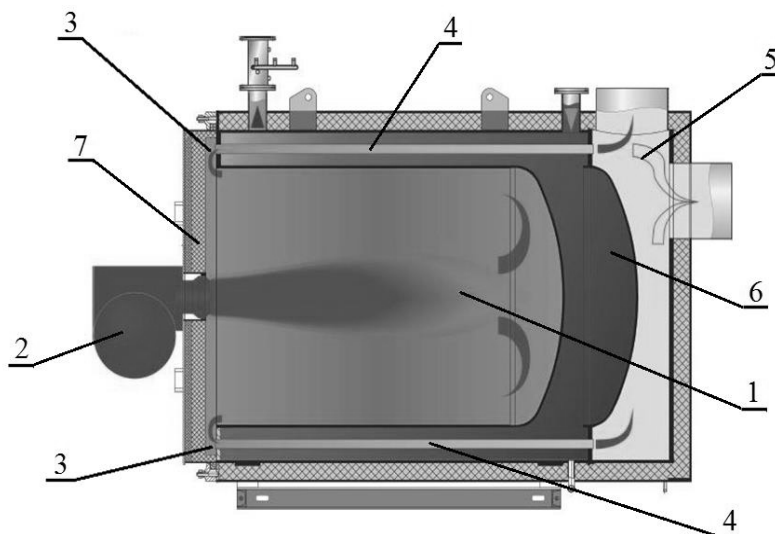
Конструктивная схема газового тракта котла ТТ-500 [1]: 1 – жаровая труба; 2 – горелка; 3 – поворотная камера; 4 – конвективный пучок дымогарных труб; 5 – сборный дымовой короб; 6 – водяной объем; 7 – крышка
